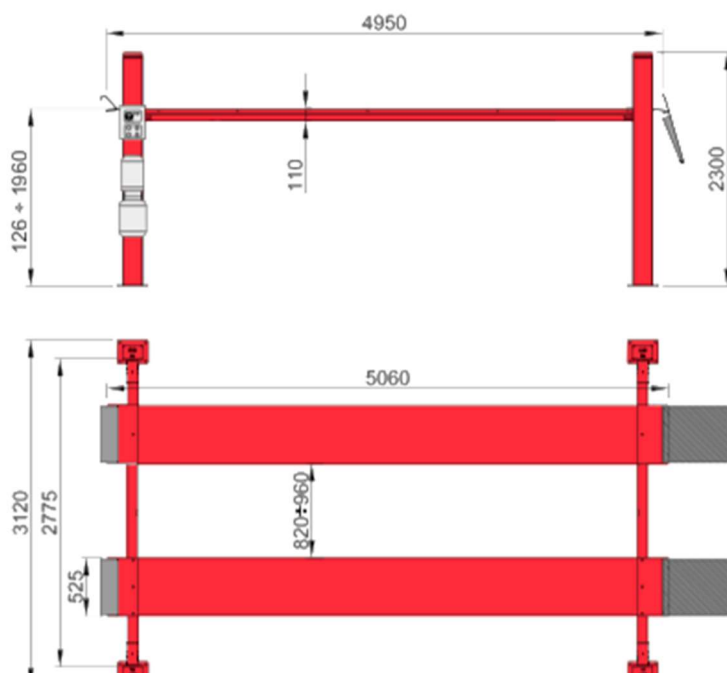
Dimensiones Elevador de 4 columnas Corghi Erco 4004B
